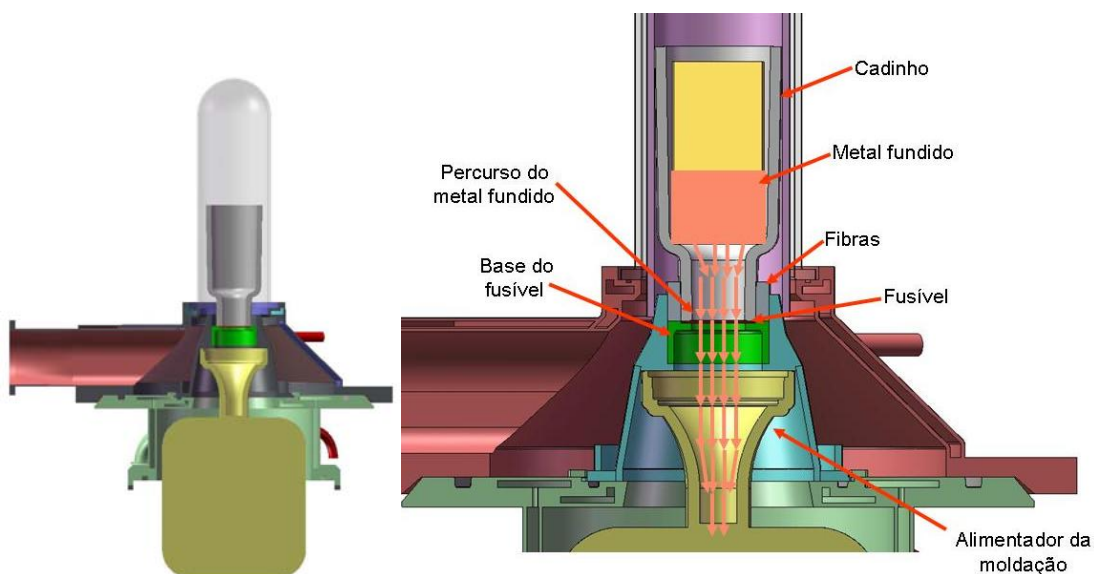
Integração da flange do fusível com a câmara de vazamento, cadinho, fusível e moldação cerâmica. Pormenor da flange com cadinho e moldação.
